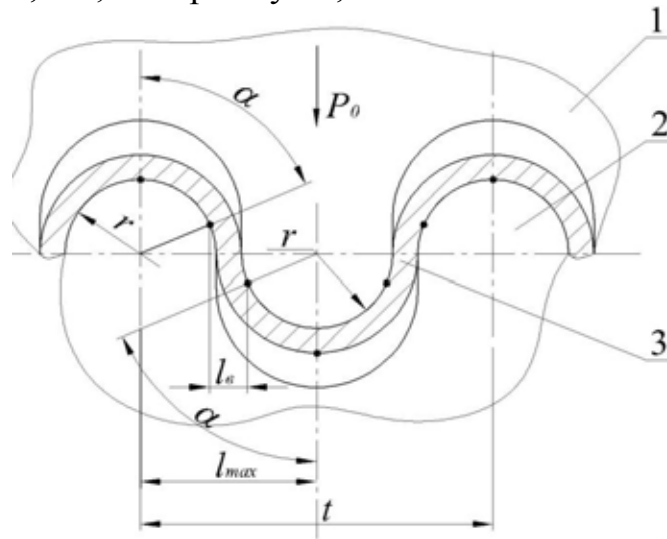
Розрахункова схема гофроутворення гвинтових заготовок колесами із спеціальним закругленим профілем зубів:
